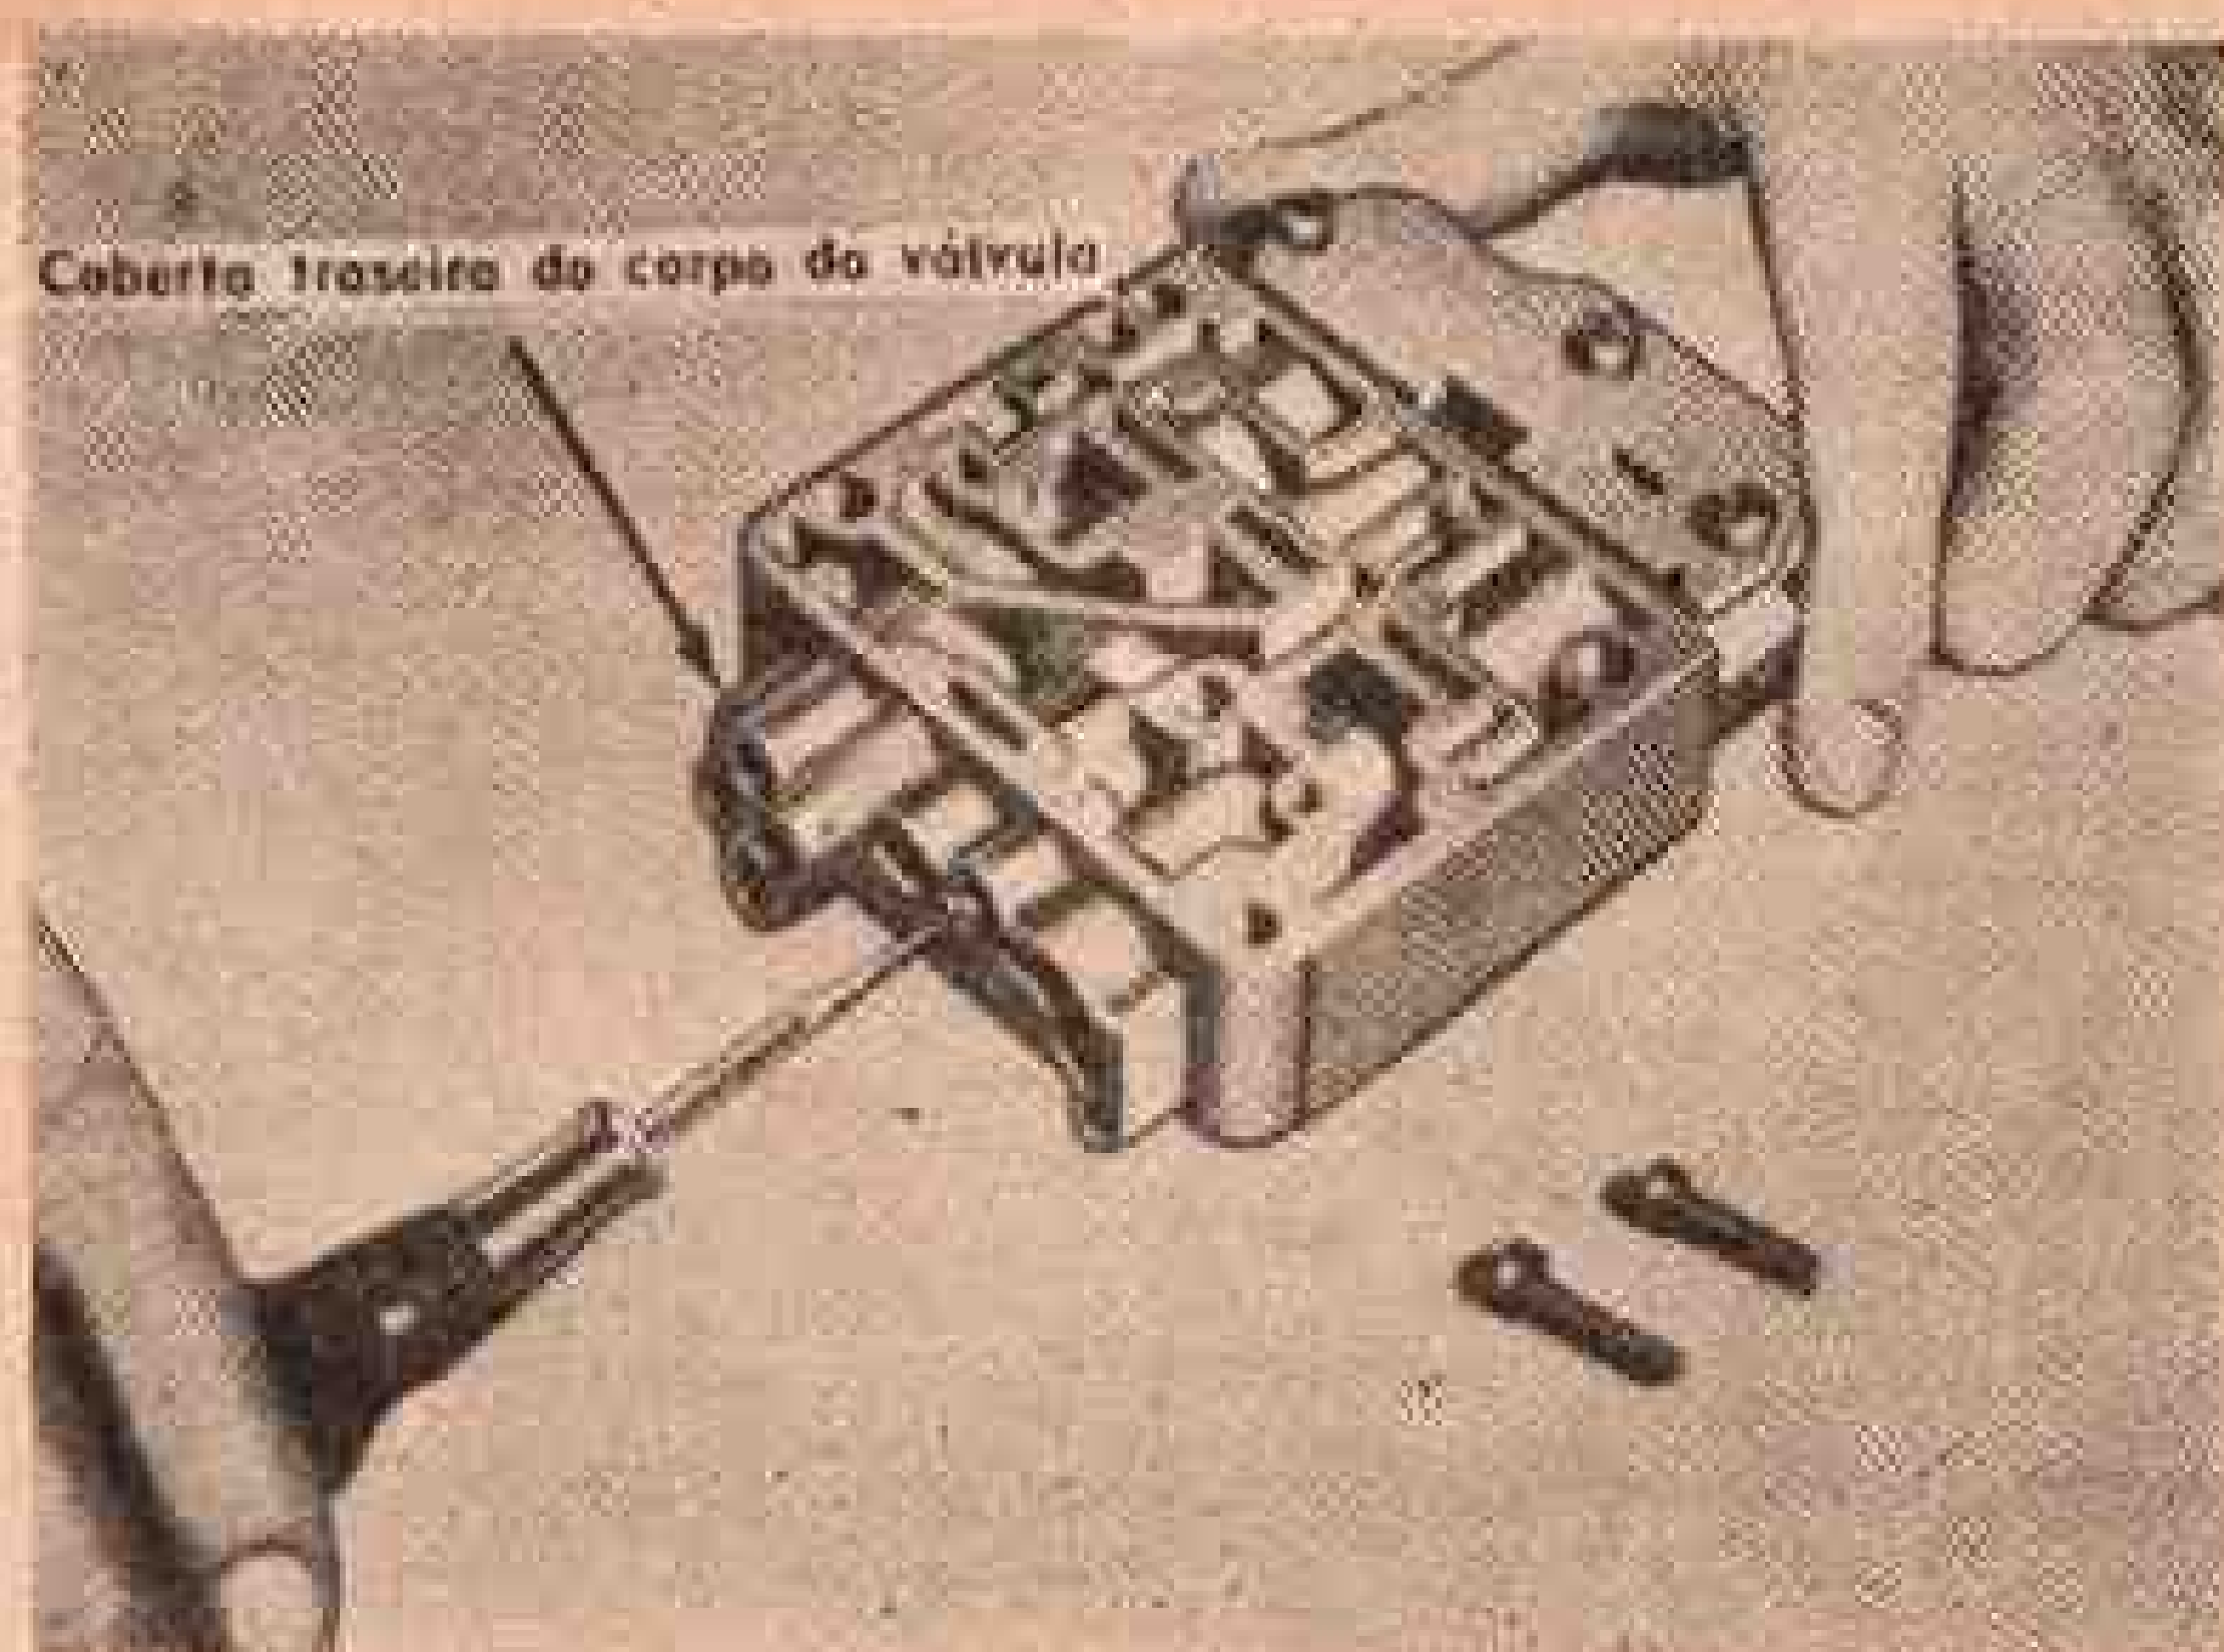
Removendo a cobertura traseira do corpo da válvula
